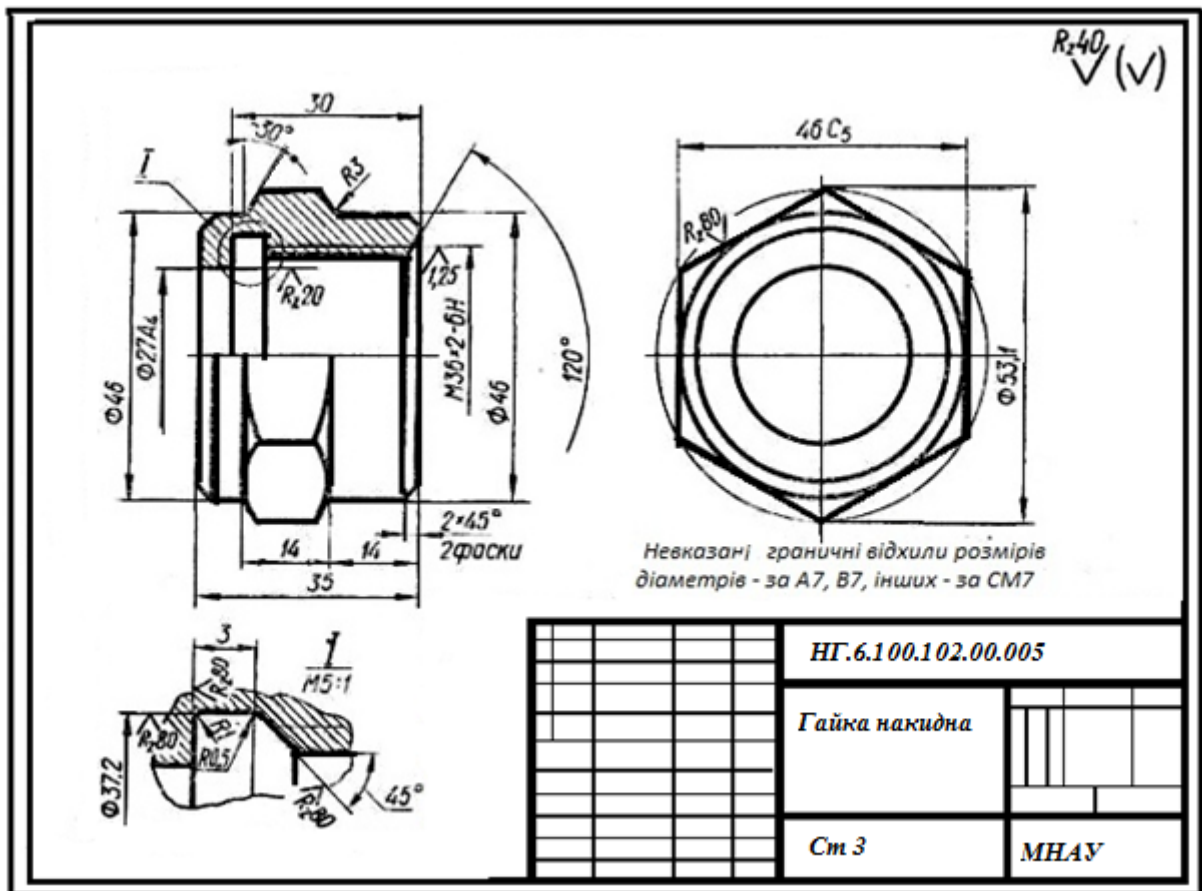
Робоче креслення деталі подвійного зворотного клапана
